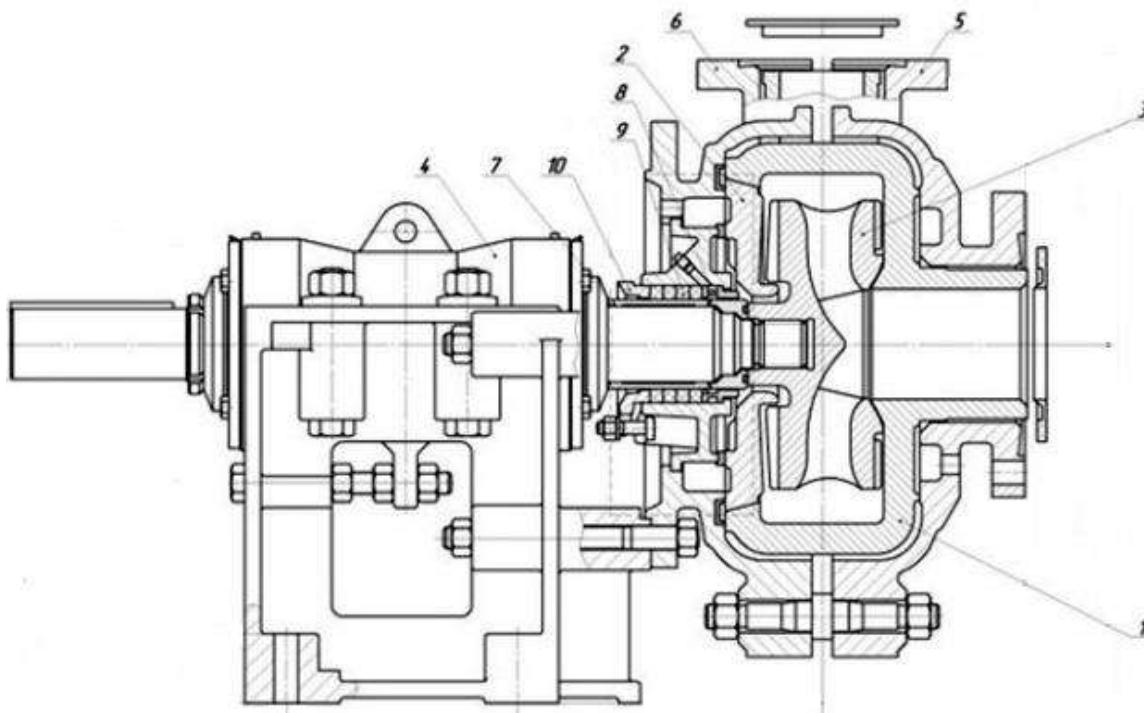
Центробежный шламовый насос WARMAN 8/6 F-АНЕ откачки щелоче-алюминатного раствора: 1 – корпус внутренний; 2 – диск защитный; 3 – колесо рабочее; 4 – стойка в сборе; 5 – корпус насоса (передняя половина); 6 – корпус насоса (задняя половина); 7 – втулка защитная; 8 – ограничитель-рассекатель; 9 – набивка многослойная; 10 – крышка сальника
